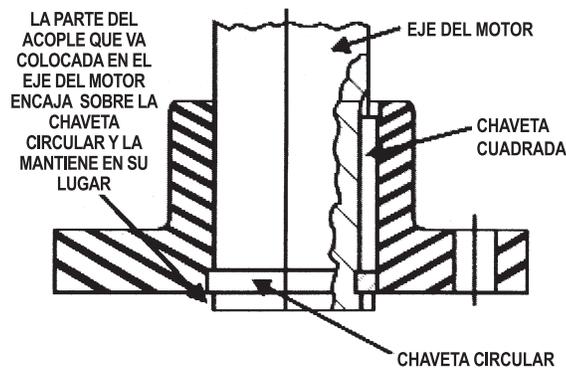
Posición Correcta de la Parte del Acople que va Colocada en el Eje del Motor
